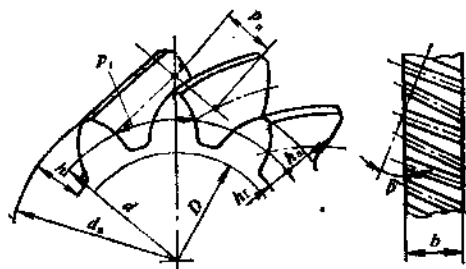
圆柱齿轮传动几何要素(斜齿轮传动)
